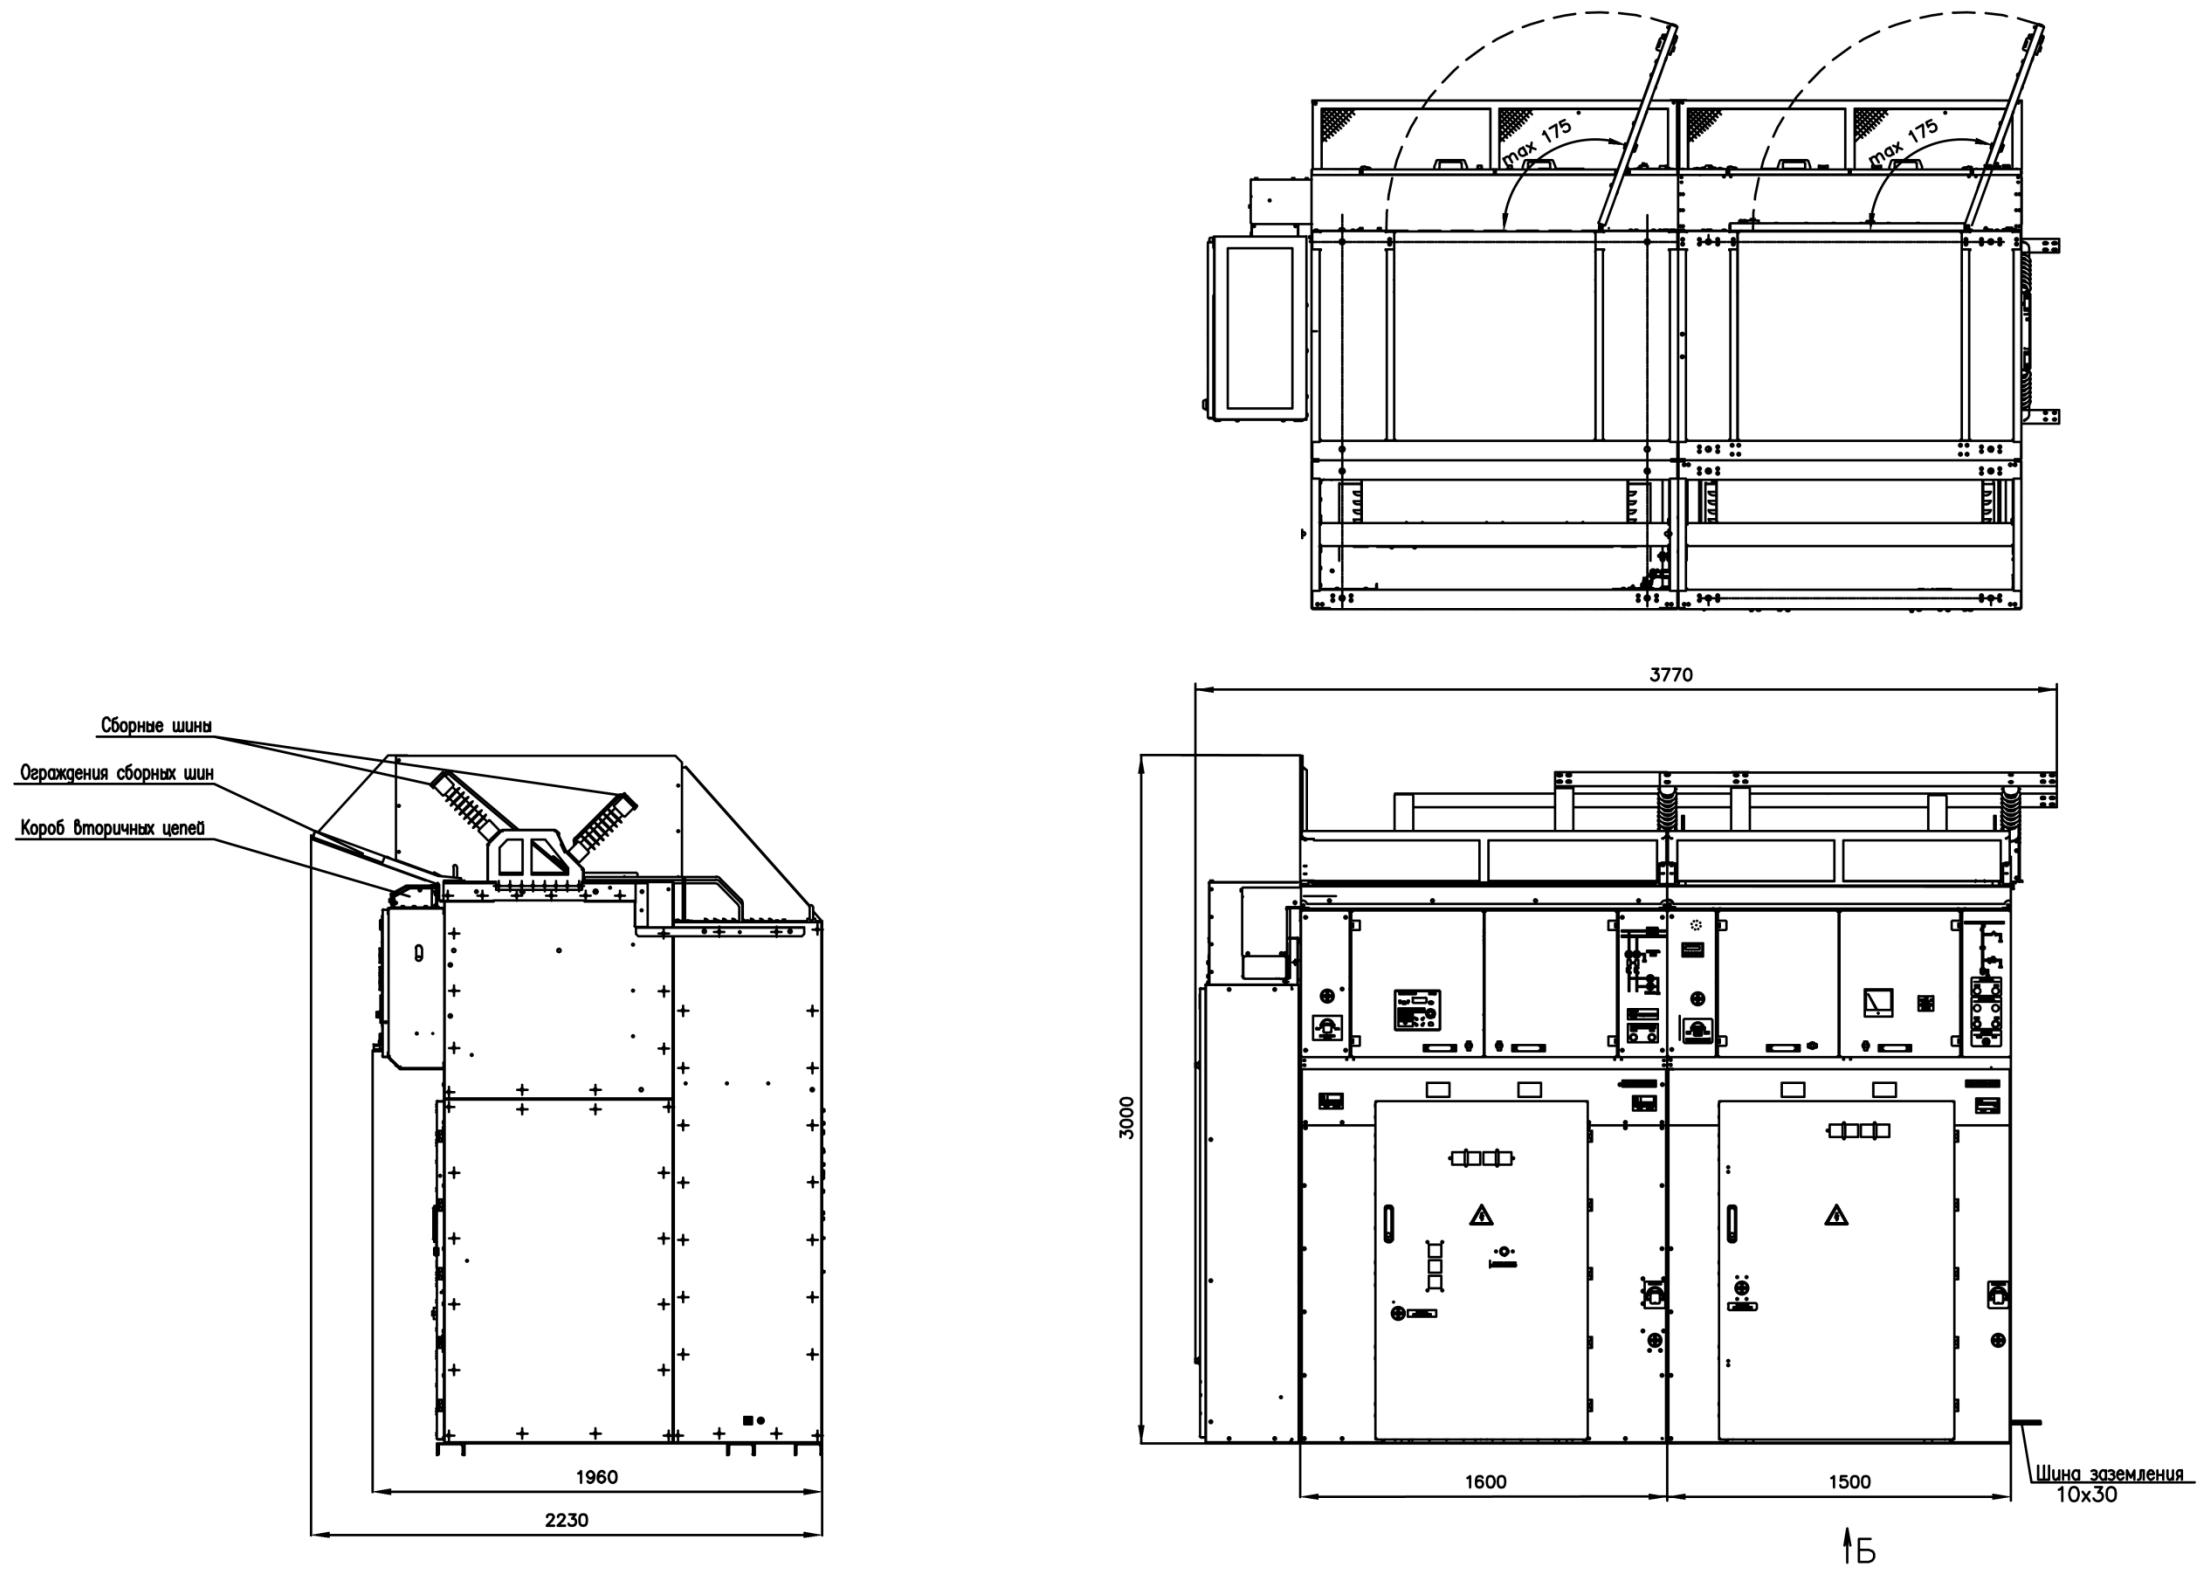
Габаритный чертеж блока КРУ (шкаф блокировок и внешних подключений – шкаф двухполюсного выключателя ввода – шкаф двух однофазных трансформаторов напряжения), масса – не более 3100 кг.
